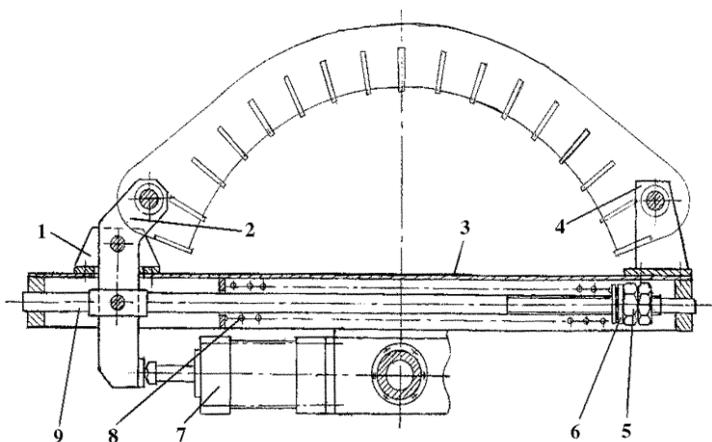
Устройство для сварки каркаса с растяжением
